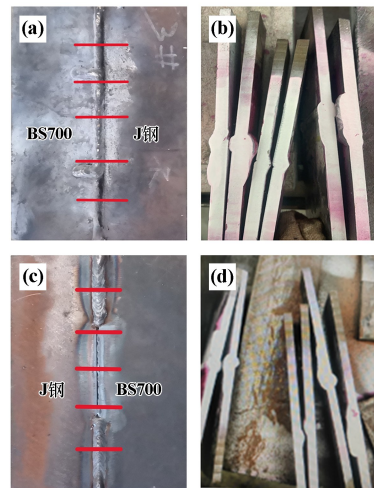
Y 型坡口焊接裂纹宏观及断面形貌
